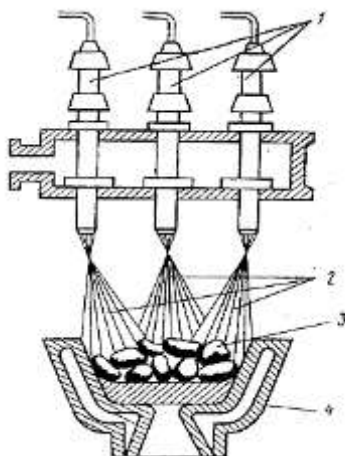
Схема ЭЛУ для переплавки металлолома:
